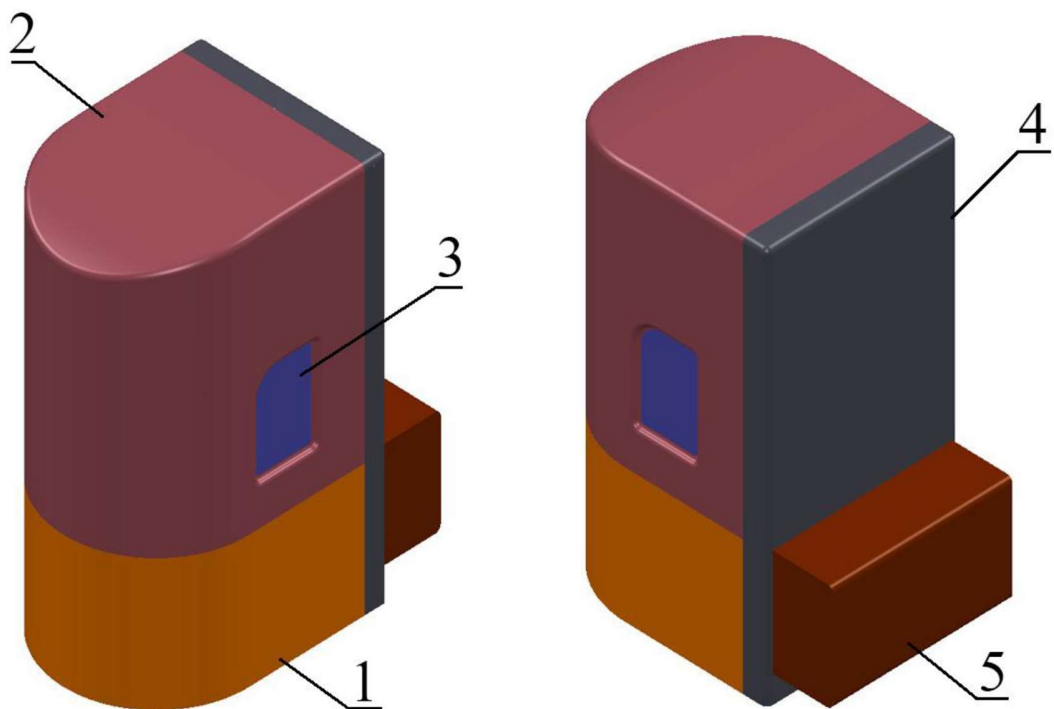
Змодельований корпус 3D сканера у PowerShape
